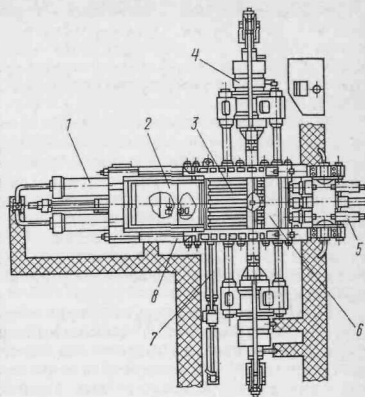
Гидравлический пакетировочный пресс Б-1642:
